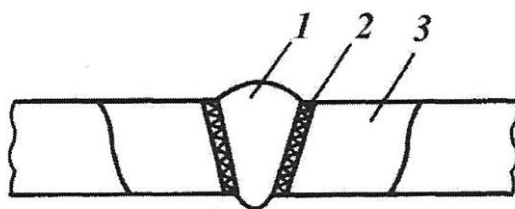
Схема строения сварного шва: 1 – сварной шов; 2 – зона сплавления; 3 – зона термического влияния
